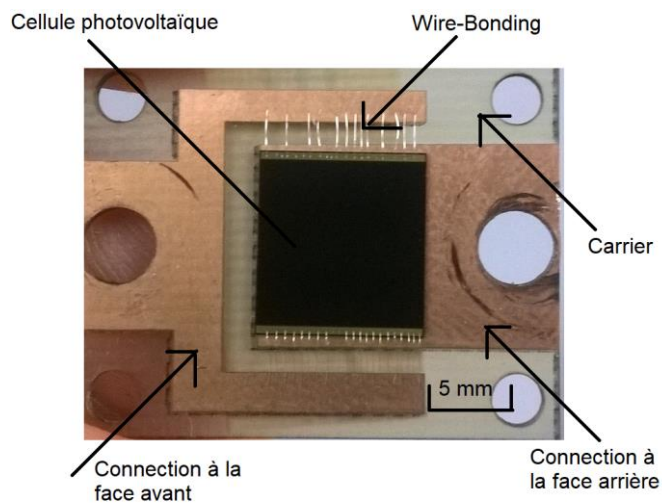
Montage sur PCB d'une cellule photovoltaïque
